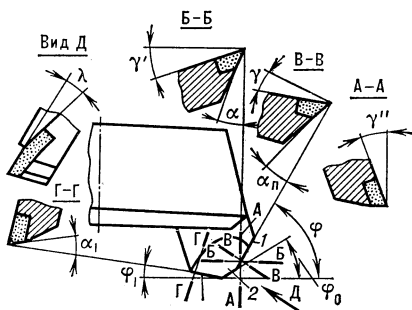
Геометрические параметры режущей части торцевой фрезы с пластинками из твёрдого сплава: 1 — главная режущая кромка; 2 — переходная режущая кромка.
